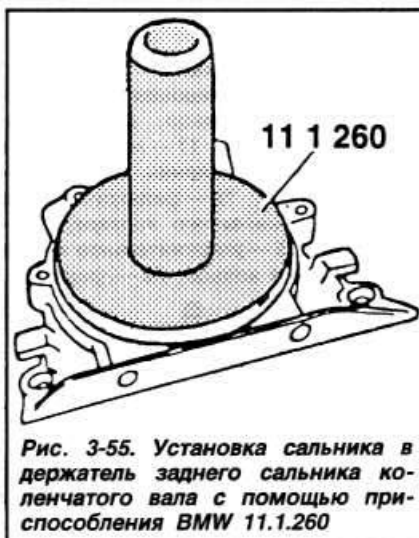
Установка сальника в держатель заднего сальника коленчатого вала с помощью приспособления BMW 11.1.260
